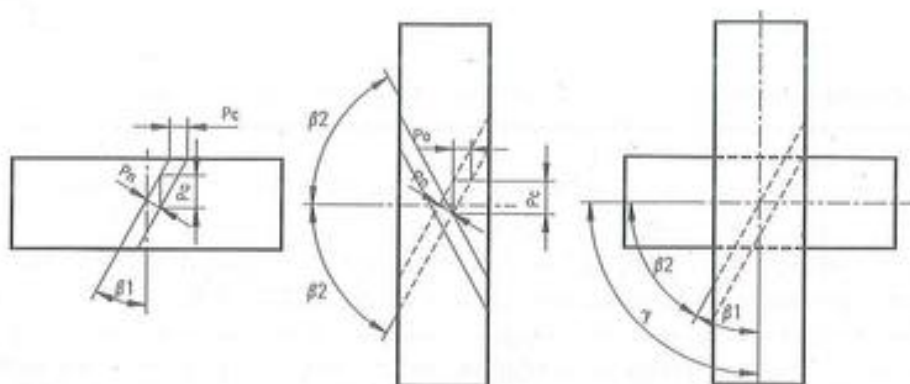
Engranajes cilíndricos helicoidales. Definiciones.
